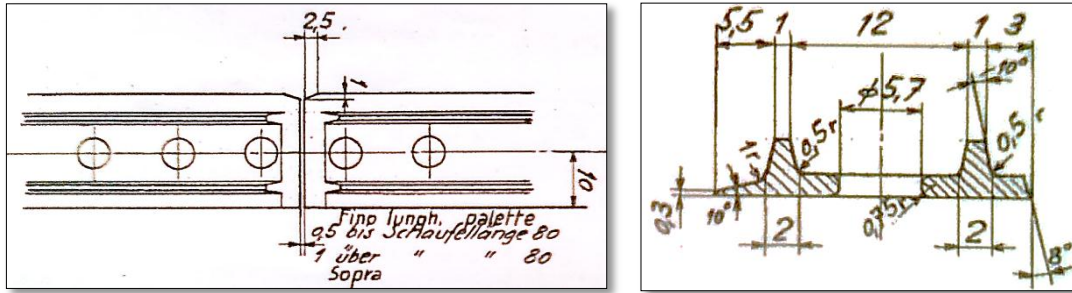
dimensioni del bendaggio del 2°, 5° e 9° stadio della macchina n° 1.
